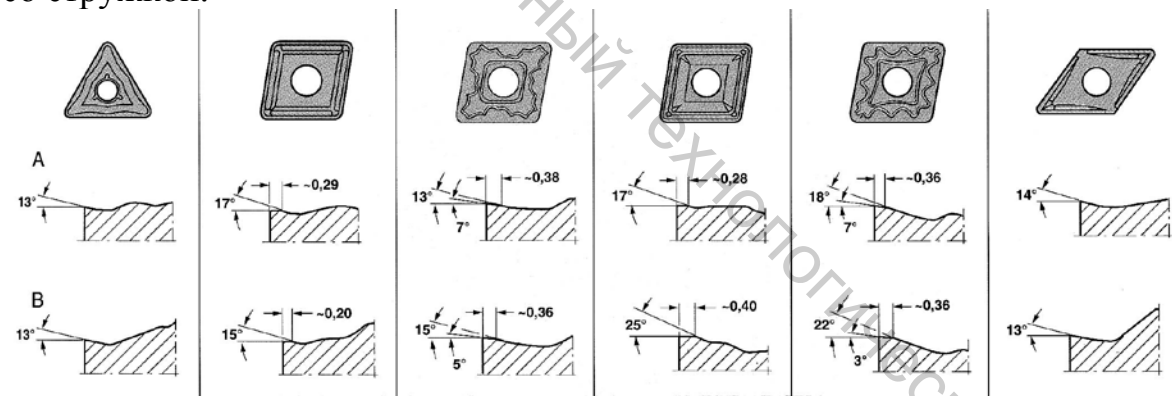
Формы передней поверхности современных режущих пластин из твердых сплавов
